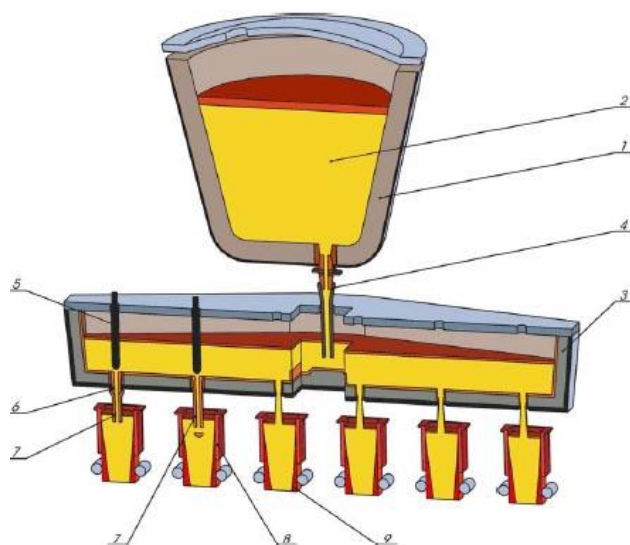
Общая схема движения металла: 1 - сталеразливочный ковш; 2 – жидкий металл; 3 – промковш; 4 – защитная труба; 5 – стопор-моноблок; 6 – стакан-дозатор; 7 – погружной стакан; 8 кристаллизатор; 9 – заготовка.
